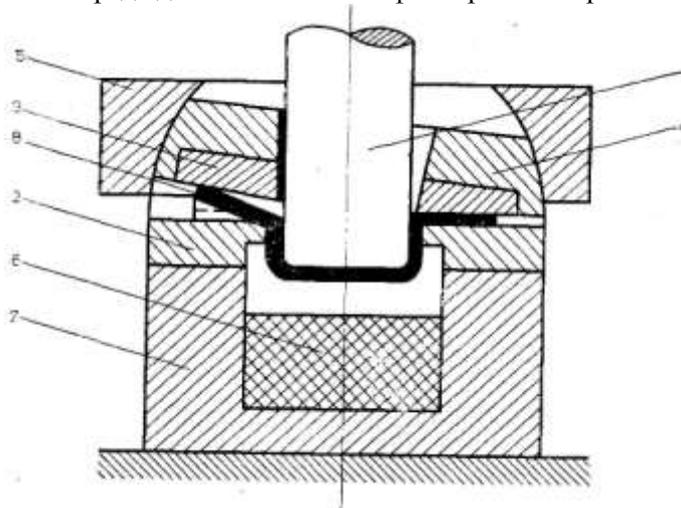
Устройство для штамповки коронок с колеблющимся прижимом (схема).
